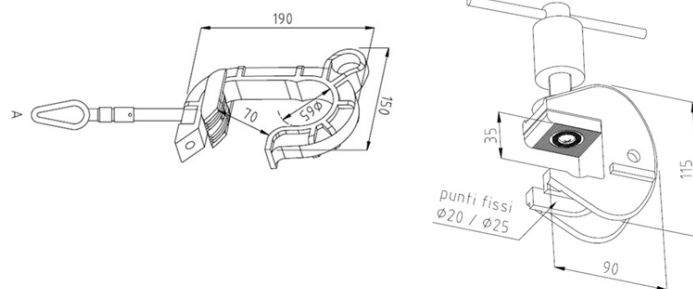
Dettaglio pinze, collegamento conduttore (sx), collegamento traliccio (dx)
